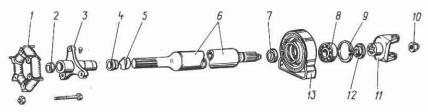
Piezas del árbol cardánico delantero: 1 - acoplamiento elástico; 2 - casquillo centrador; 3 - brida del acoplamiento elástico; 4 - retén; 5 collar del retén; 6 - árbol cardánico; 7 - guarda-
